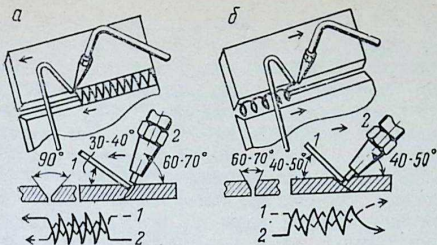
Левая (а) и правая (б) газовая сварка:
